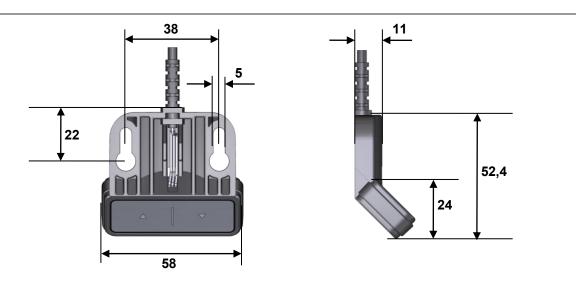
Bedienelement TOUCHbasic-down, Montagemaße (Angaben in mm)
